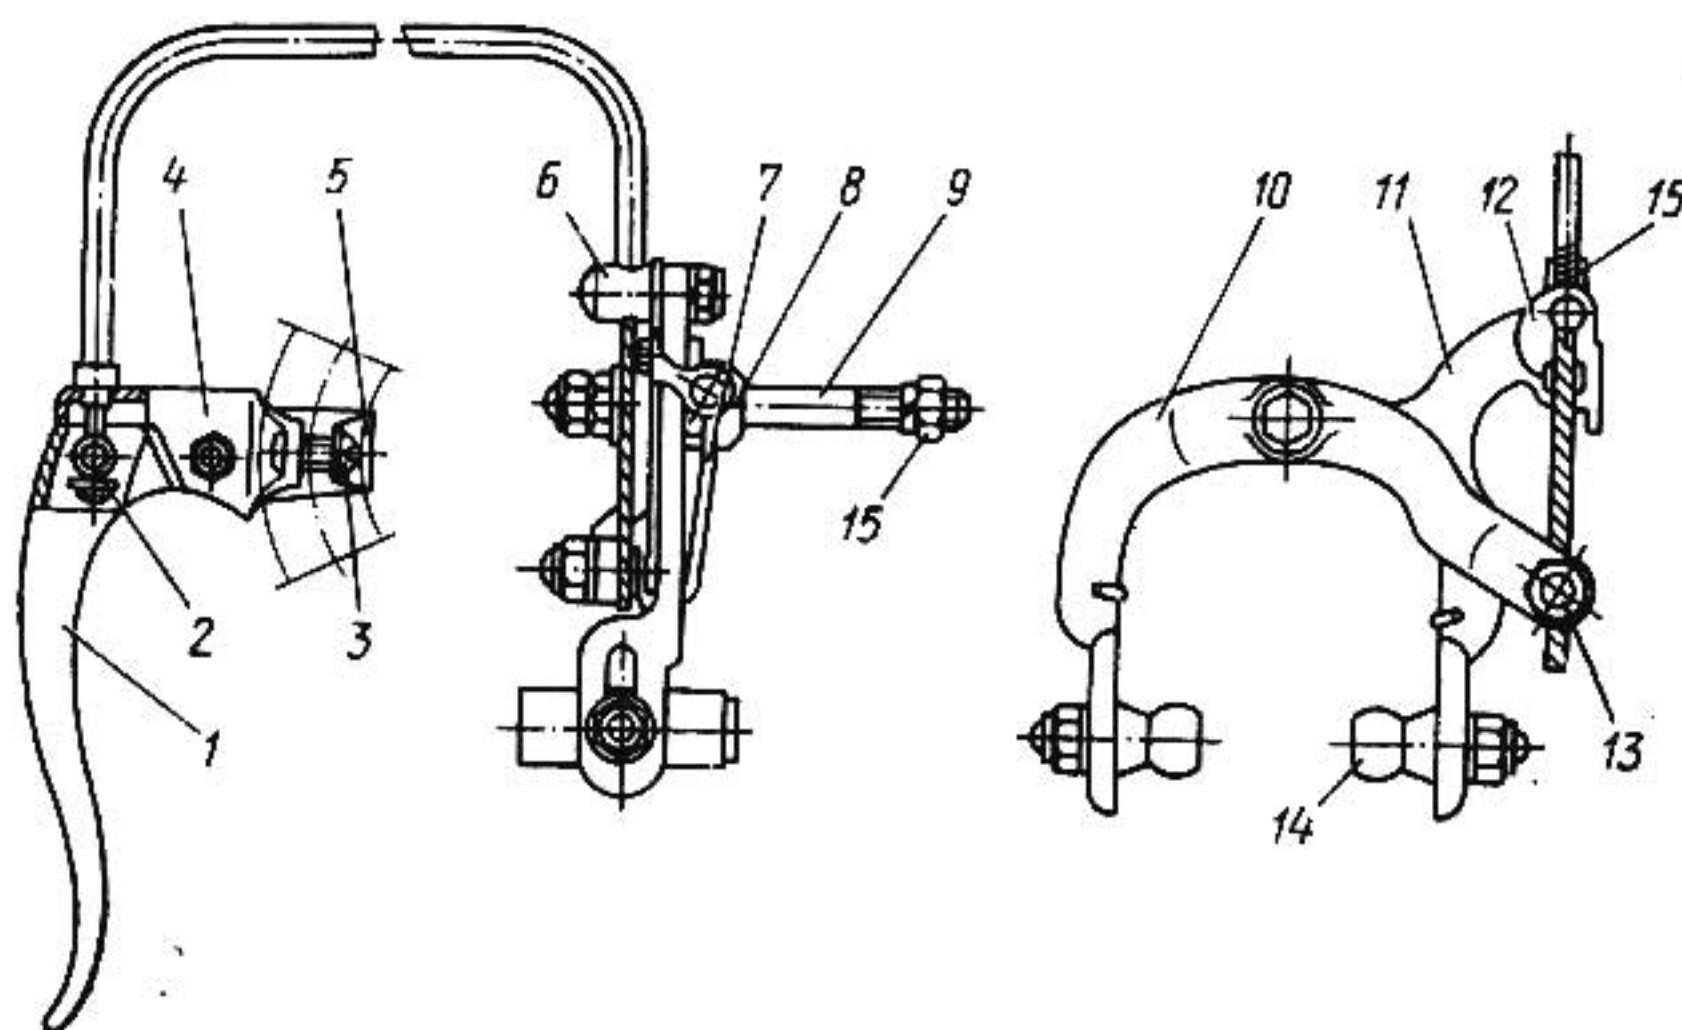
Ручной клещевой тормоз с боковой тягой:
